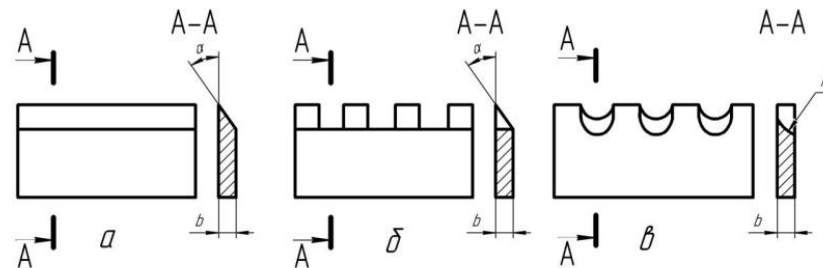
Види ножів подрібнювачів коренеплодів: а - плоский ніж; б - гребінчастий (дифузійний); в - совочкоподібний ніж; α - кут заточування;
